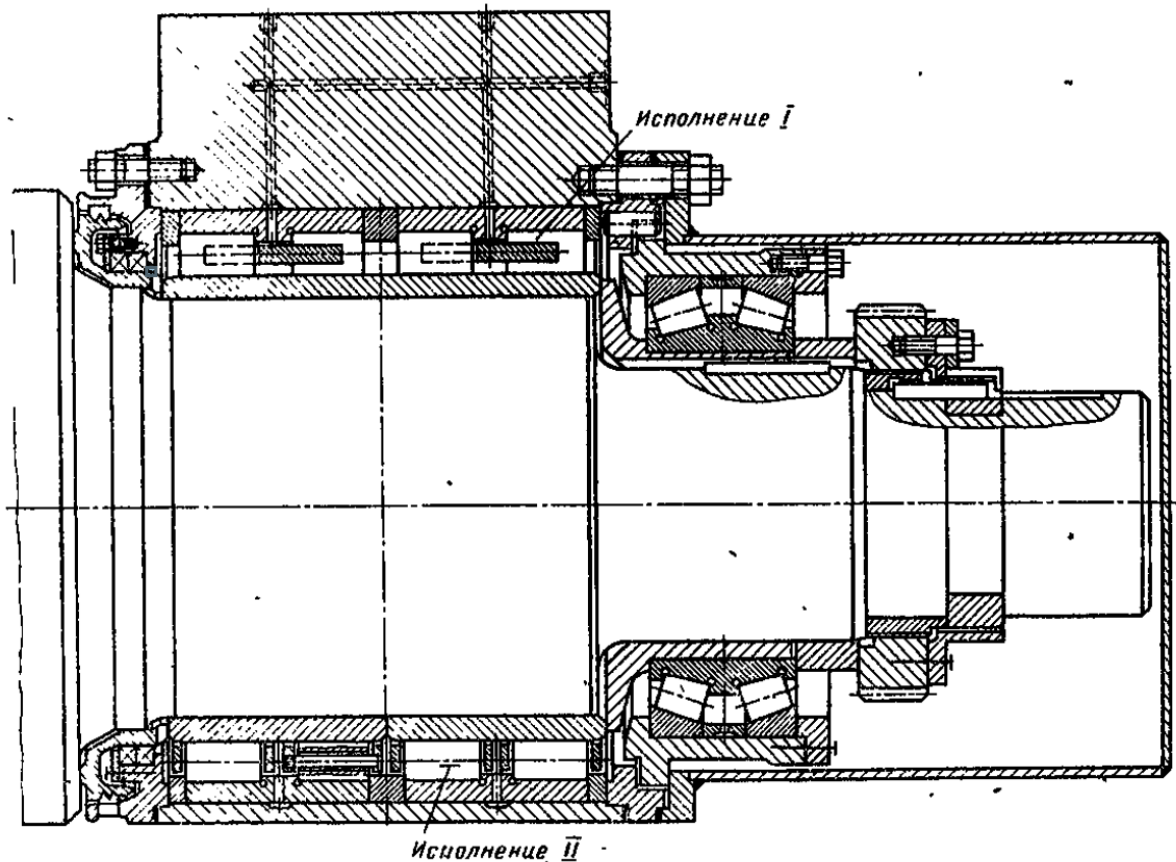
Опора прокатного валка на багаторядному підшипнику із циліндричними роликами.
